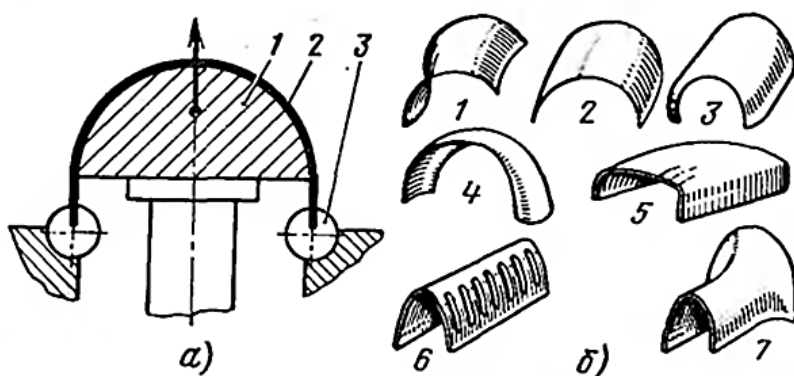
а - схема поперечної обтяжки; 1 - пуансон; 2 - заготовка; 3 - затискні клеми; б - типові деталі, виготовлені на пресі ОП-3; 1, 3, 7 - деталі, виготовлені в спареному вигляді шляхом повторної обтяжки по одному і тому ж пуансону з проміжною термообробкою; 2, 4, 5 - деталі, виготовлені за одну
